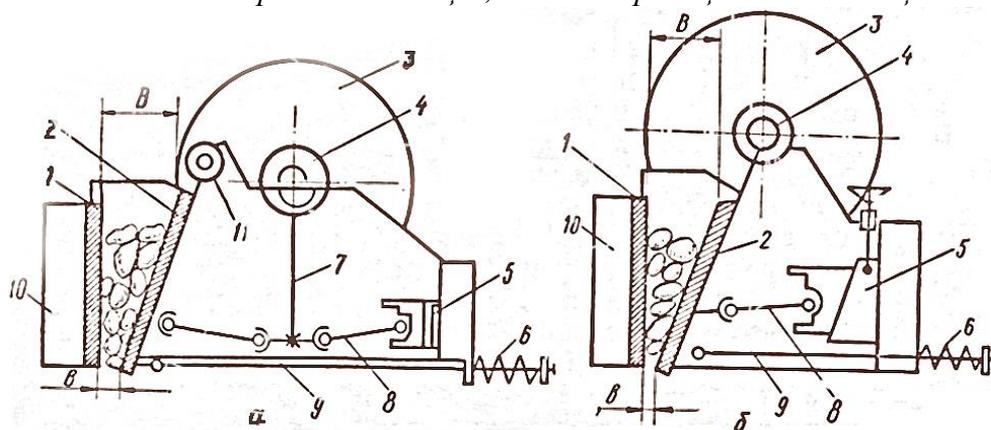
Конструктивные схемы щековых дробилок простым (а) и сложным (б) движением щеки: 1, 2 – неподвижная и подвижная щеки; 3 – маховик; 4 – эксцентриковый (главный) вал; 5 – гнездо упора распорных плит; 6 – пружины замыкающего механизма; 7 – шатун; 8 – распорная плита; 9 – тяга замыкающего механизма; 10 – станина; 11 – ось подвеса подвижной щеки; в – ширина разгрузочной щели (минимальная)
